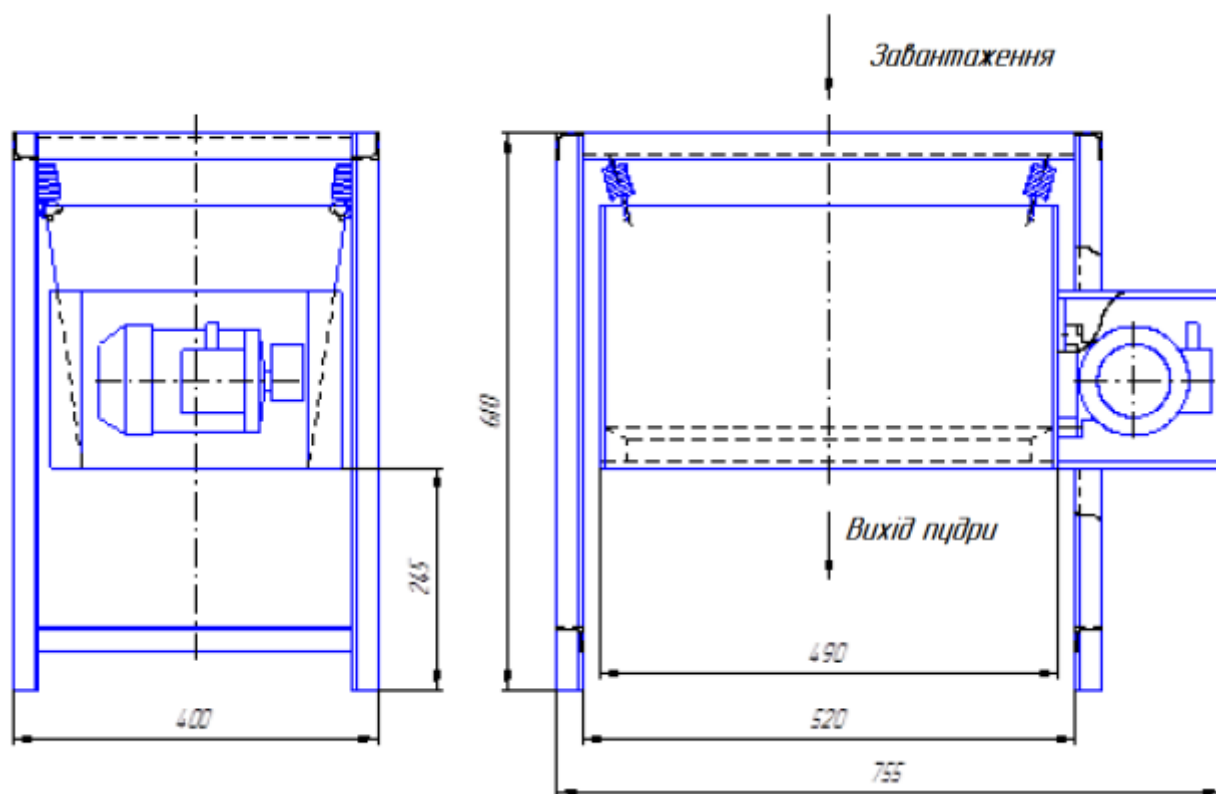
7 – Пристрій для опудрювання зефіру 7956К-18
